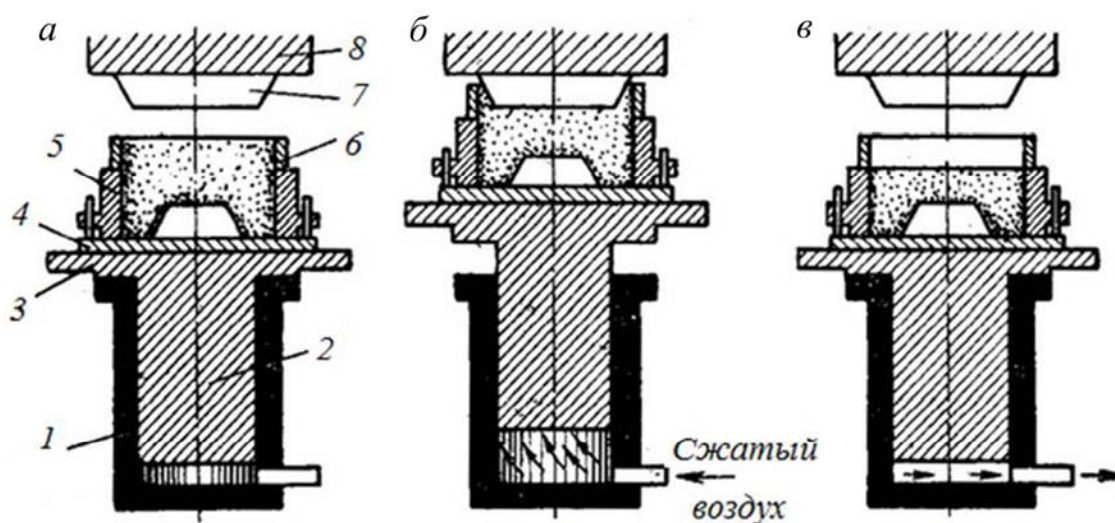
Процесс уплотнения смеси на прессовой формовочной машине с верхним прессованием:
